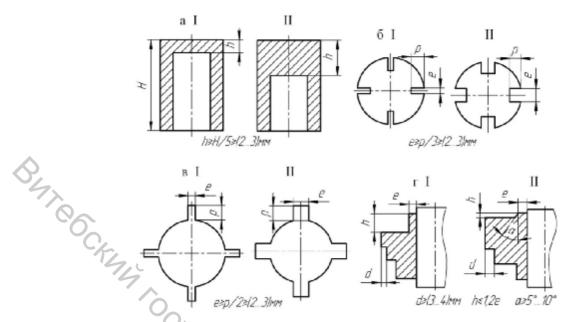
Нерациональные (I) и рациональные (II) конструкции порошковых деталей: а – с глухими отверстиями; б – с продольными пазами; в – с продольными выступами;  $\varepsilon$  – ступенчатых.
